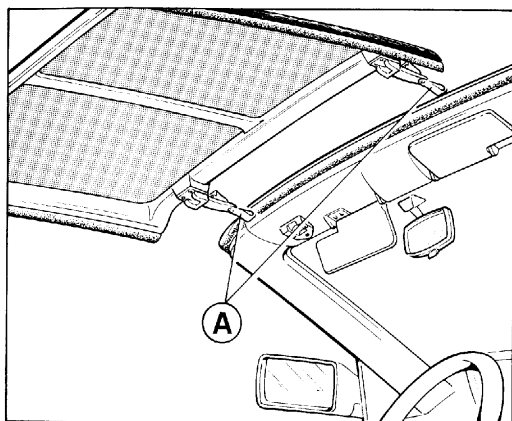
26 - 27 - Tettuccio rigido (smontaggio e rimontaggio)
